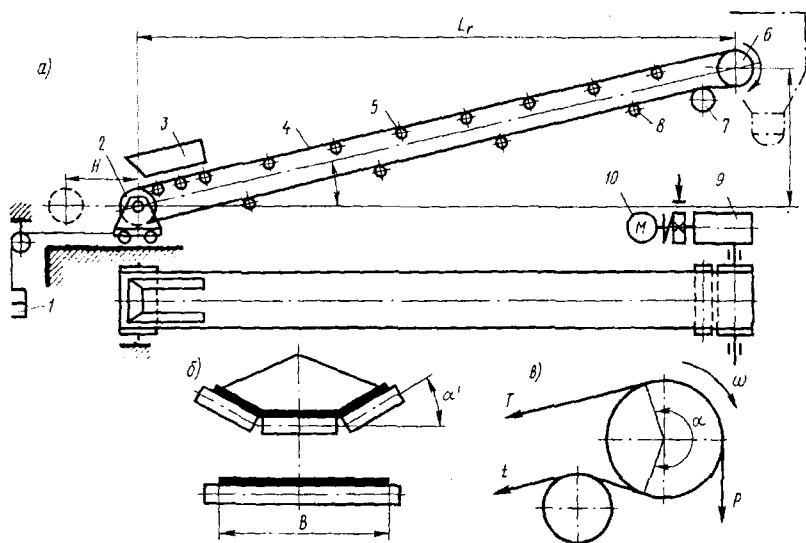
Ленточный конвейер: а – схема конструкции; б – роlikоопоры; в – схема усилий на приводном барабане; 1 – натяжное устройство; 2 – натяжной барабан; 3 – воронка; 4 – лента; 5 – верхняя роlikоопора; 6 – приводной барабан; 7 – отклоняющий барабан; 8 – нижняя роlikоопора; 9 – редуктор; 10 – электродвигатель.
